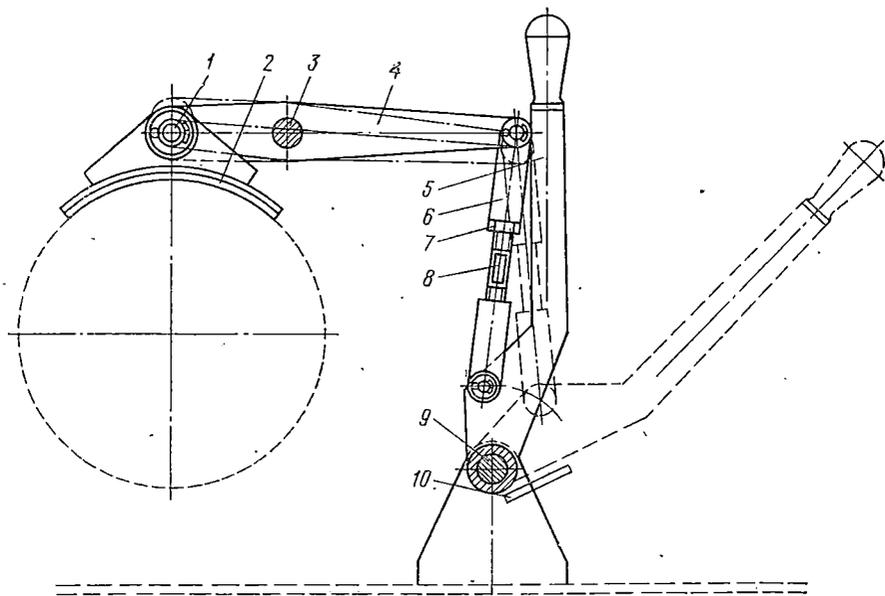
Тормоз хода и поворота экскаваторов Э-302Б и Э-304Б:
